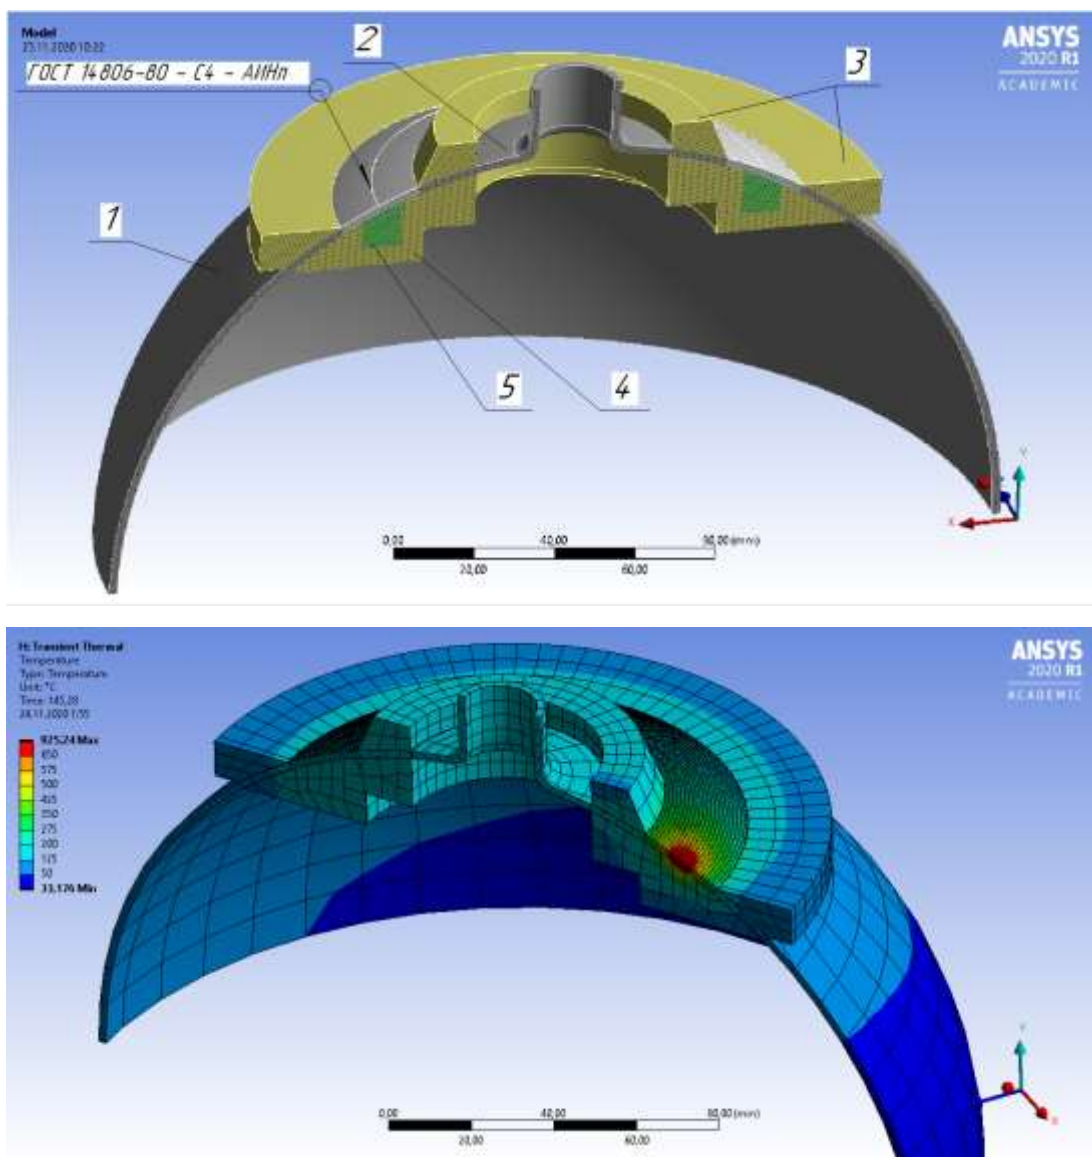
Пример реальной сварной конструкции (1 – полусфера, 2 – горловина, 3 и 4 – сборочно-сварочная оснастка из аустенитной стали, 5 – сменный элемент сборочно-сварочной оснастки из аустенитной стали).
